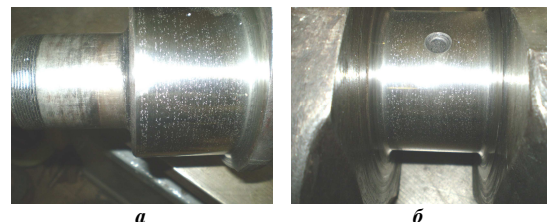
Загальний вид робочої поверхні корінної та шатунної шийки сталевого колінчастого валу двигуна 4ЧН 12/14 після зміцнення:
